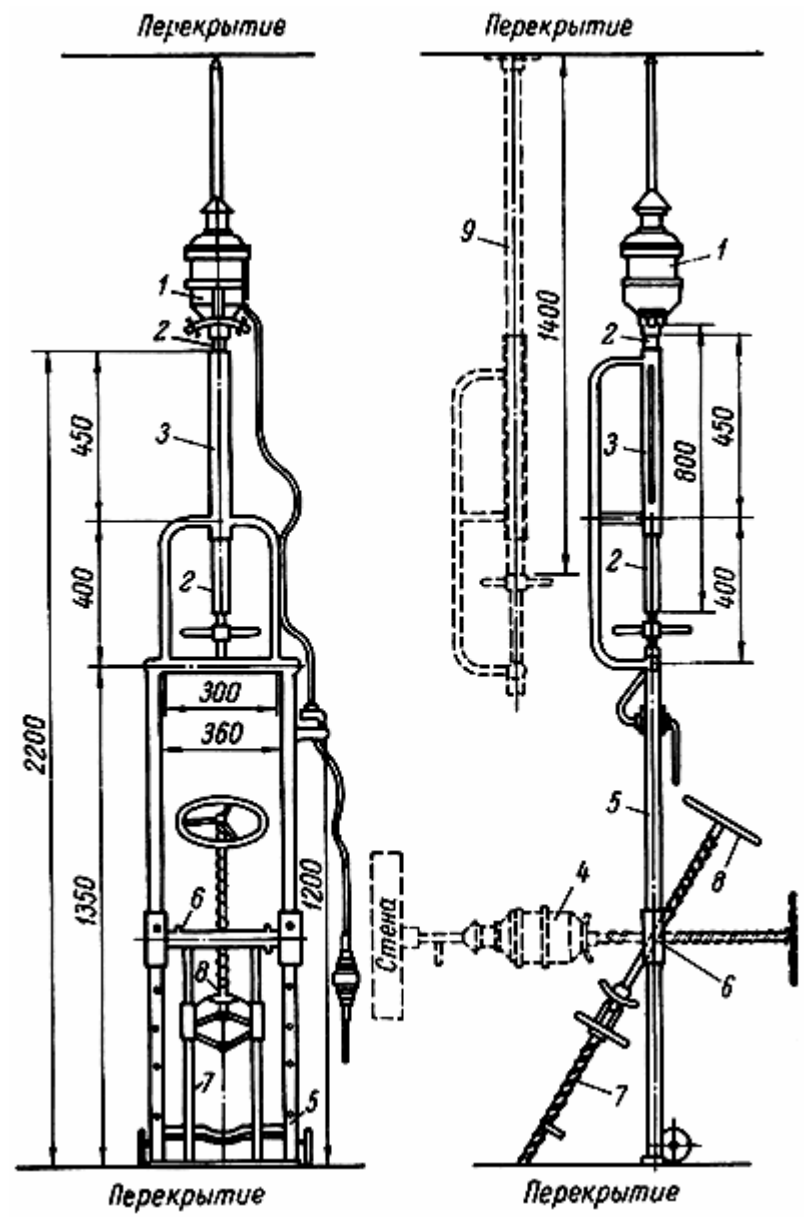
Станок-стойка для сверления отверстий в полах, потолках и стенах
